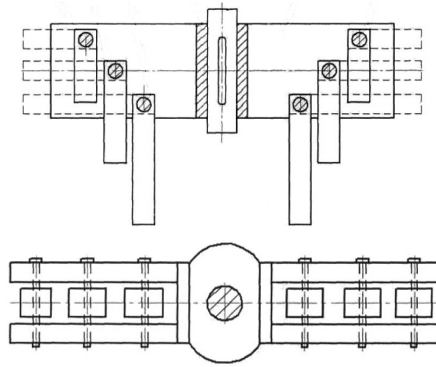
Лопатева мішалка згідно з пат. № UA102233U
